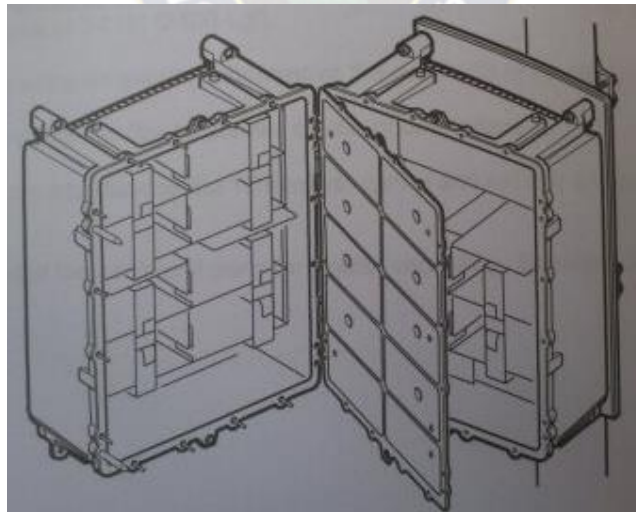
PBC-MU y PBC-BU correctamente montadas (Fuente: Instrucciones de instalación Ericsson 2111).
